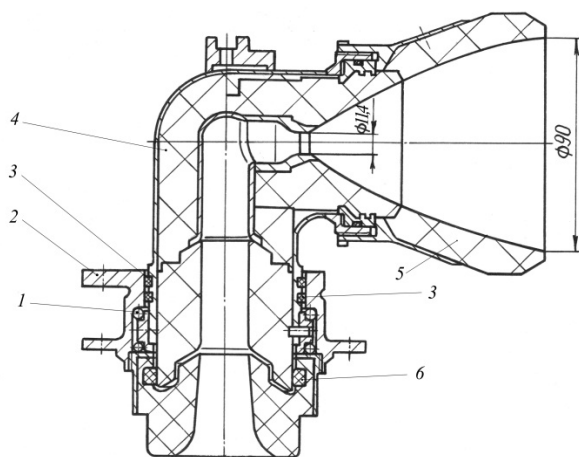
Конструкция вращающегося сопла двигателя 15Д171:
